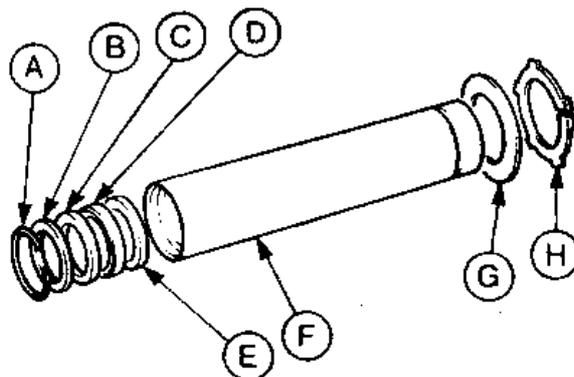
Порядок установки манжет и стопорных колец (Разд.35)
